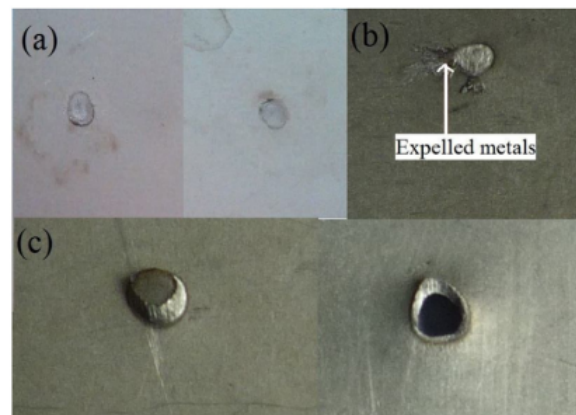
Three types of welding joints with different failure: (a) Schlecht mit IF (b) Spritzer mit IF (c) Gut mit PF
